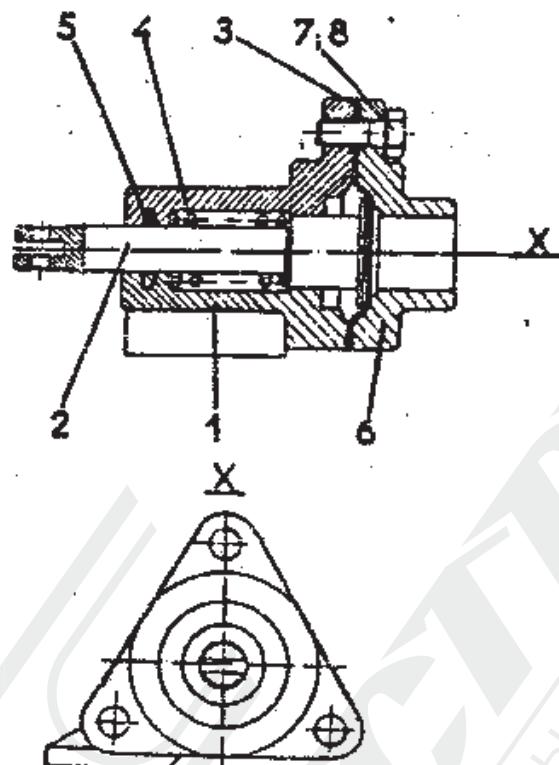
Пневматический двигатель отключающий привод коробки скоростей.
